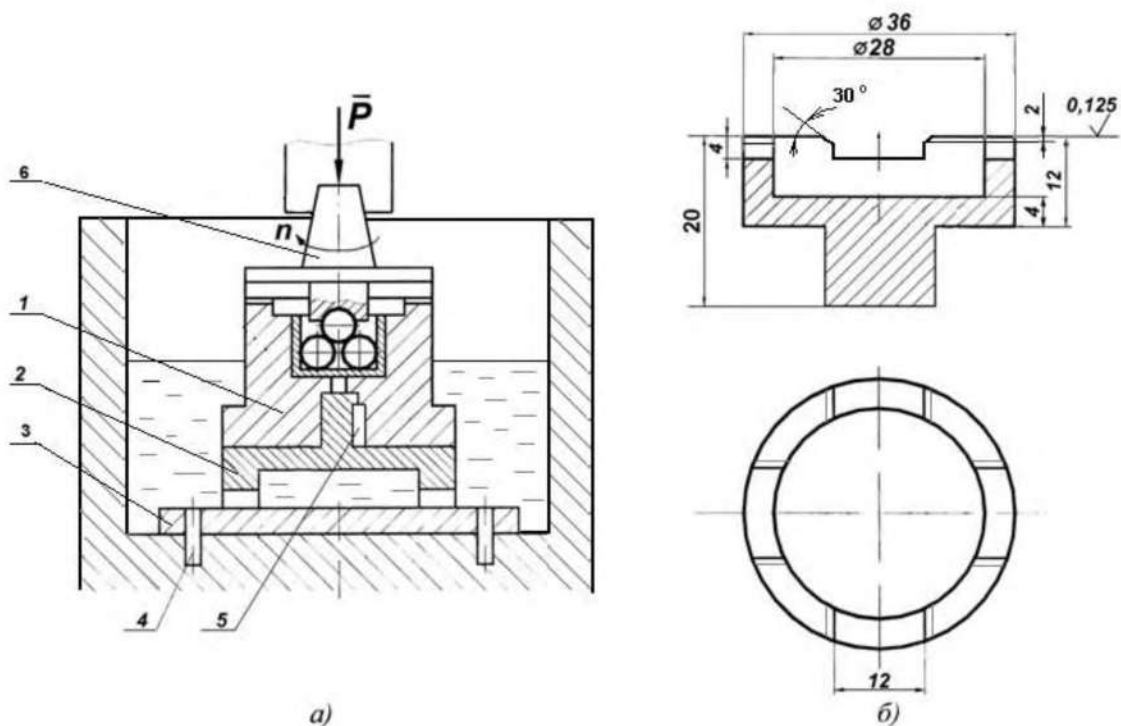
Схема кріплення, конструкція зразка: 1 – оправка; 3 – контртіло; 2 – зразок, що досліджується; 4 – штифт; 6 – хвостовик; 5 – шпонка.
